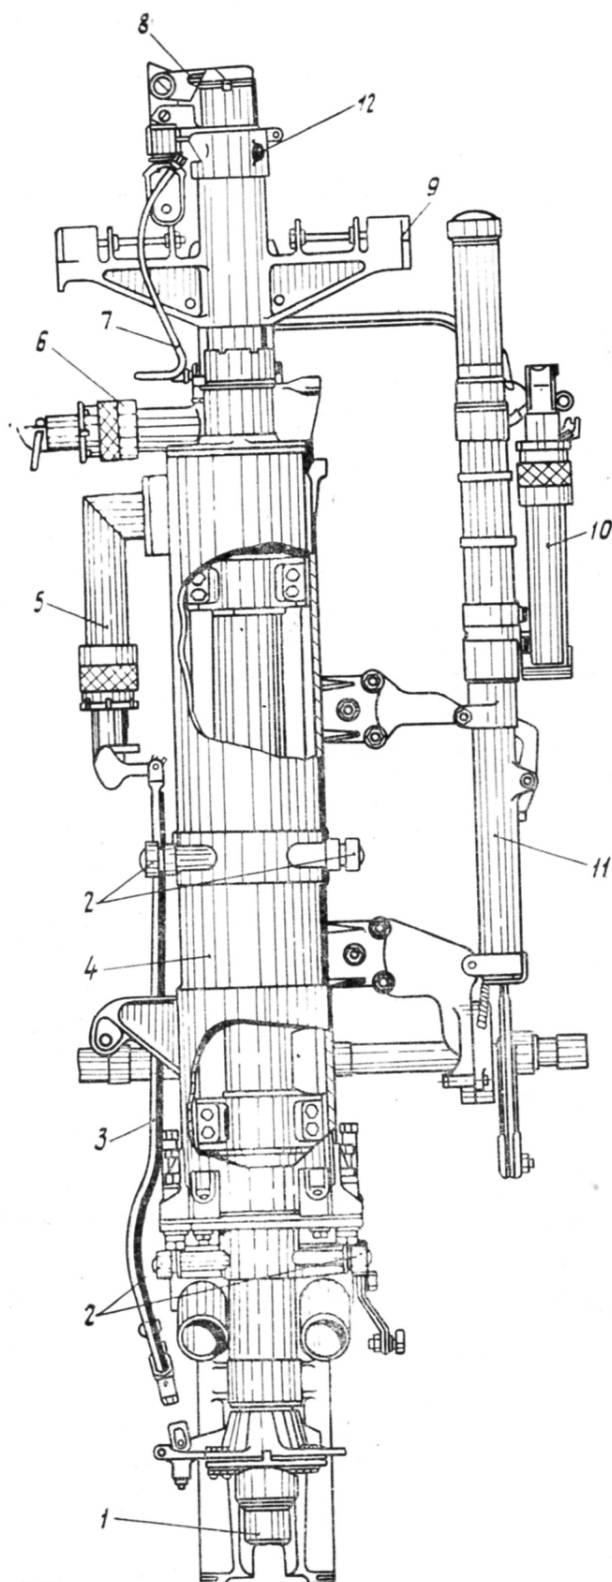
Комбинированный стреляющий механизм КСМ: 1—стреляющий механизм СМ; 2—ролик; 3—раздвижная тяга; 4—пороховой ускоритель; 5—воспламенитель; 6—пиромеханизм парашютного механизма; 7—трубка; 8—парашютный механизм; 9—балка; 10—пиромеханизм аварийного притяга плеч; 11—механизм аварийной системы плечевого притяга; 12—дюза
